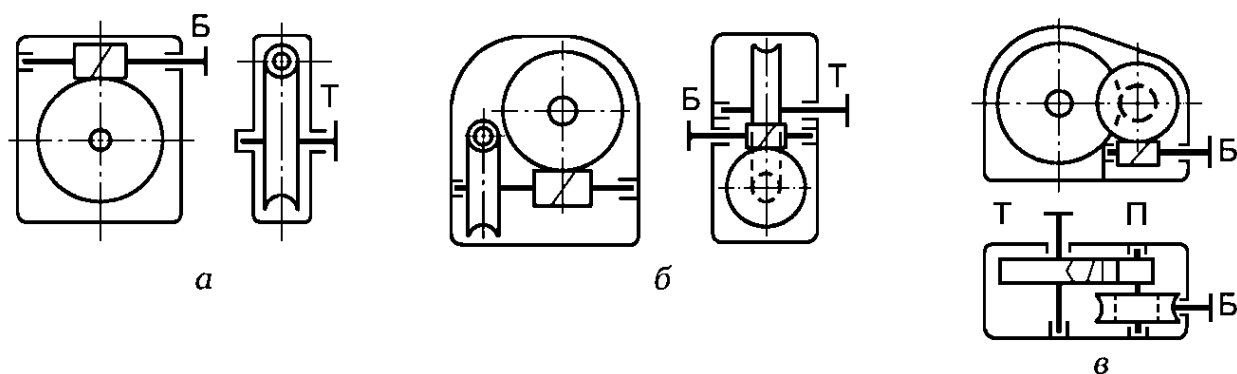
Схемы червячных редукторов: *а* – одноступенчатый; *б* – двухступенчатый; *в* – червячно-цилиндрический
